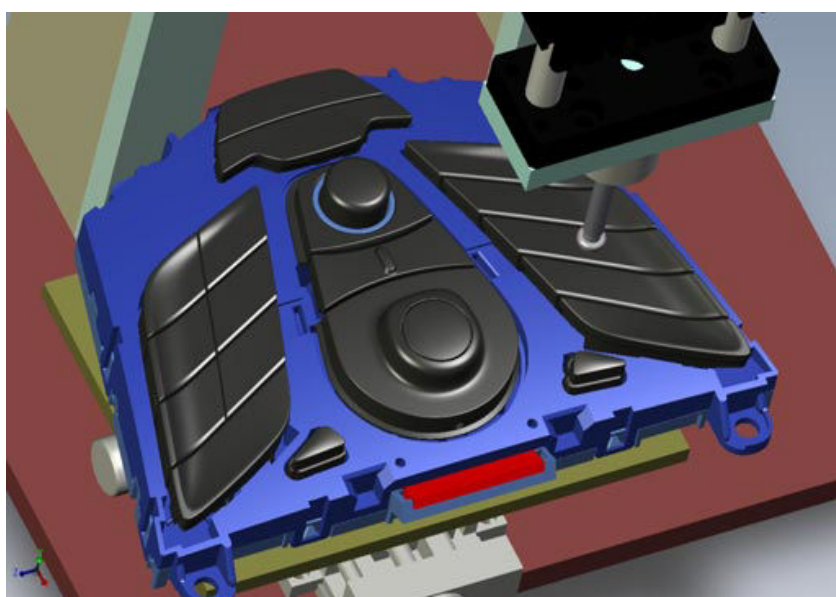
Prüflingsbaugruppe mit Bedientasten und Drehstellern
